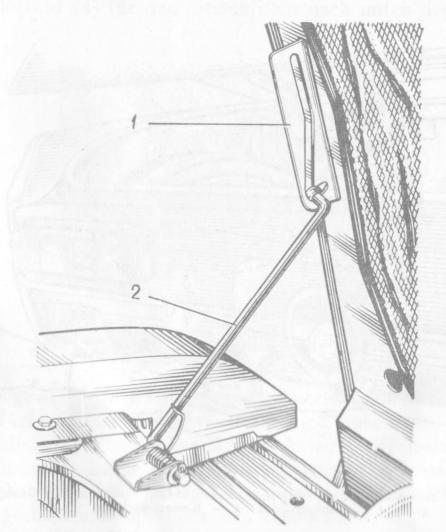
Motorhaubenstütze: 1 — Motorhaubenkulisse; 2 — Anschlagstütze
